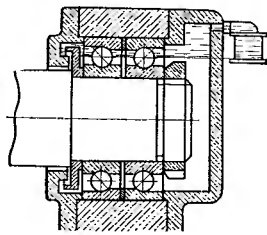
Сливное отверстие в крышке корпуса тихоходного подшипника
